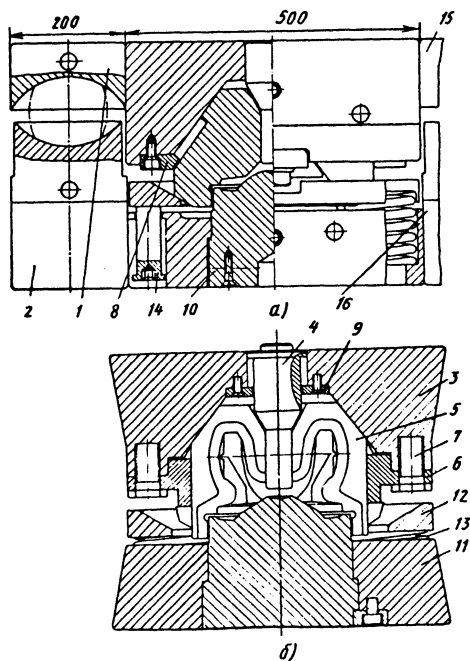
Закрытый штамп с разъемной матрицей для безоблойной штамповки поковки фланца-вилки карданного вала:
